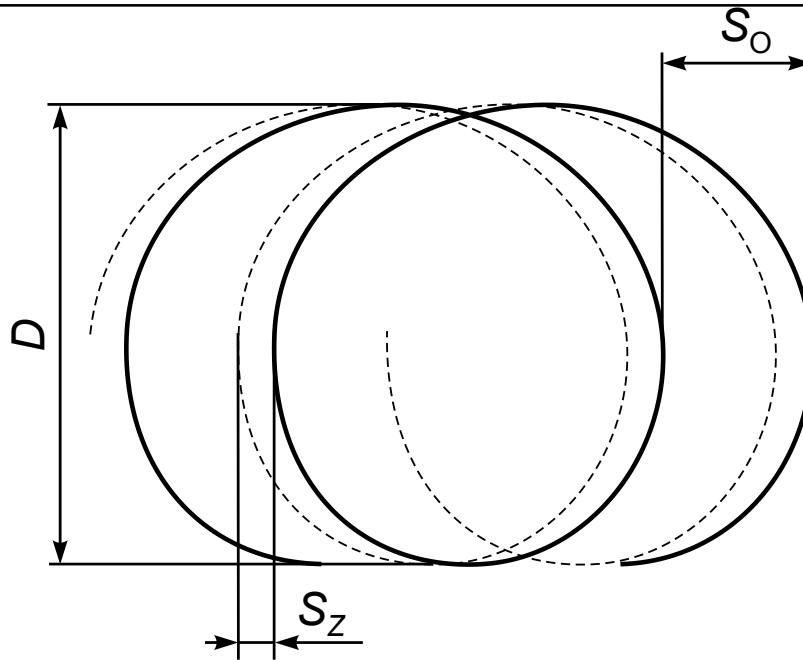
Траектории рабочих движений двух смежных зубьев осевой цилиндрической фрезы (для  $z = 4$  и  $S_o = 0,32 D$ )
